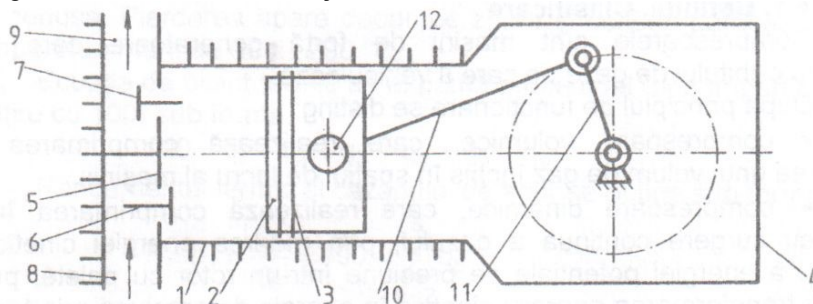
Schema constructivă a unui compresor cu piston:
